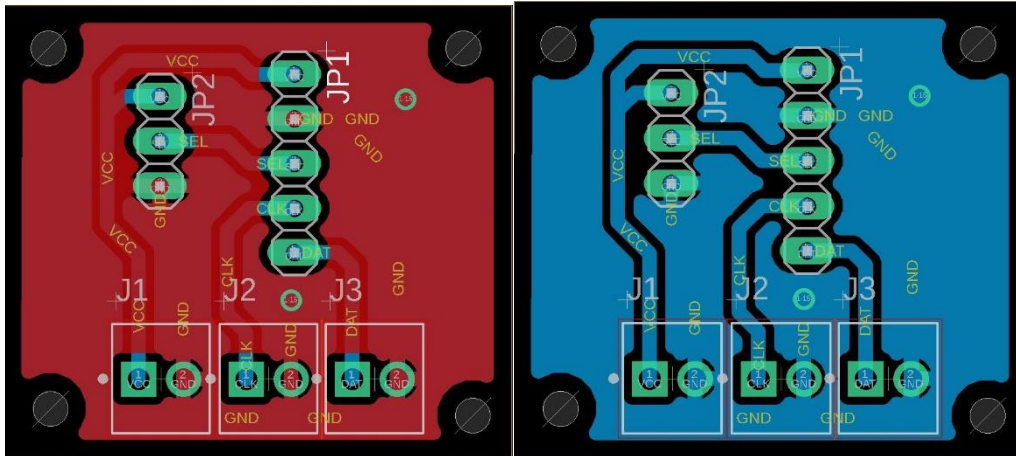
(a)Diseño PCB micrófonos cara TOP (izquierda). Fig. 30: (b)Diseño PCB micrófonos cara BOTTOM (derecha).
